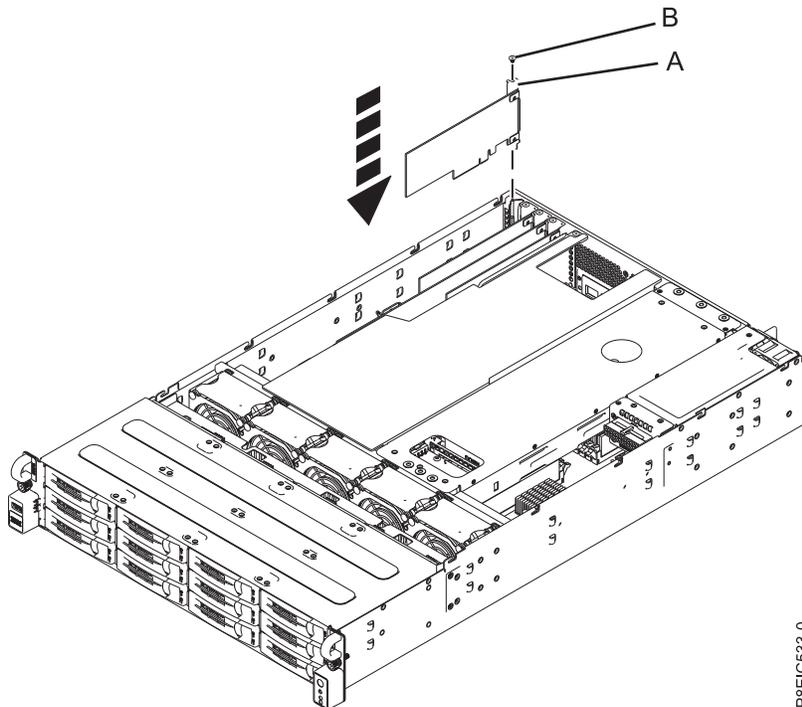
Instalando o adaptador PCIe (A) e parafuso (B)
